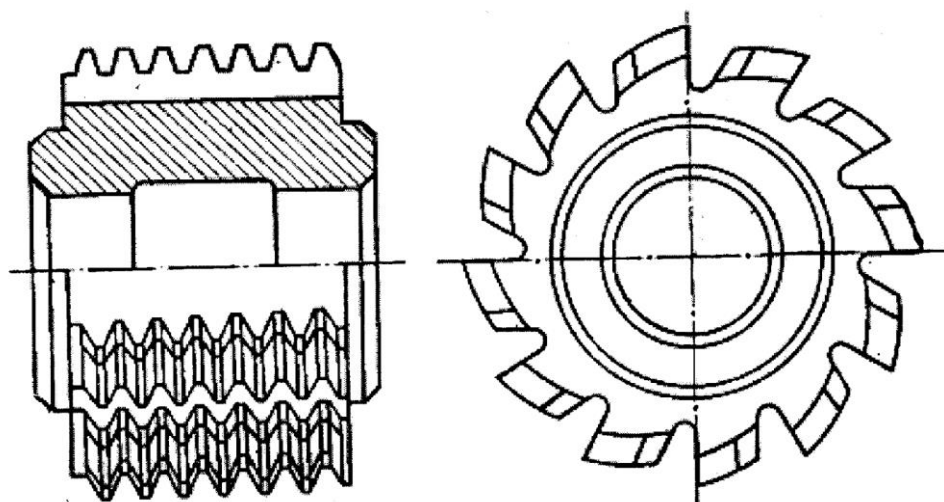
Фреза червячная мелко модульная для цилиндрических зубчатых колес с эвольвентным профилем. ГОСТ 10331
